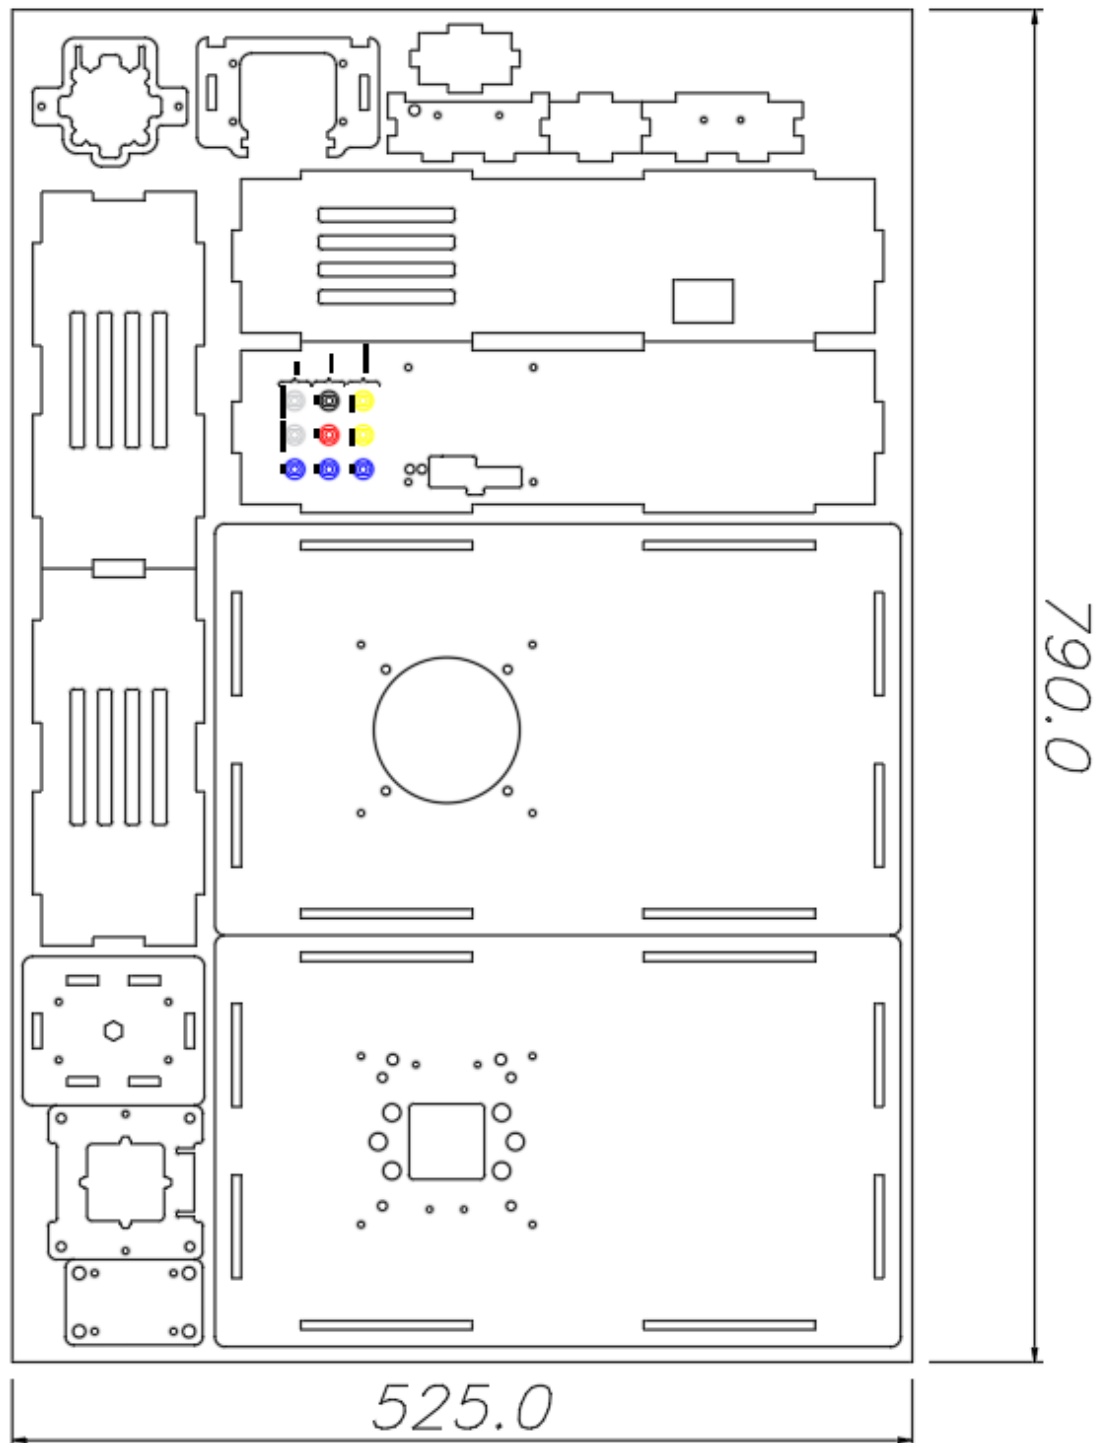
Plano mecanizado estructura puesto de prácticas en metacrilato
